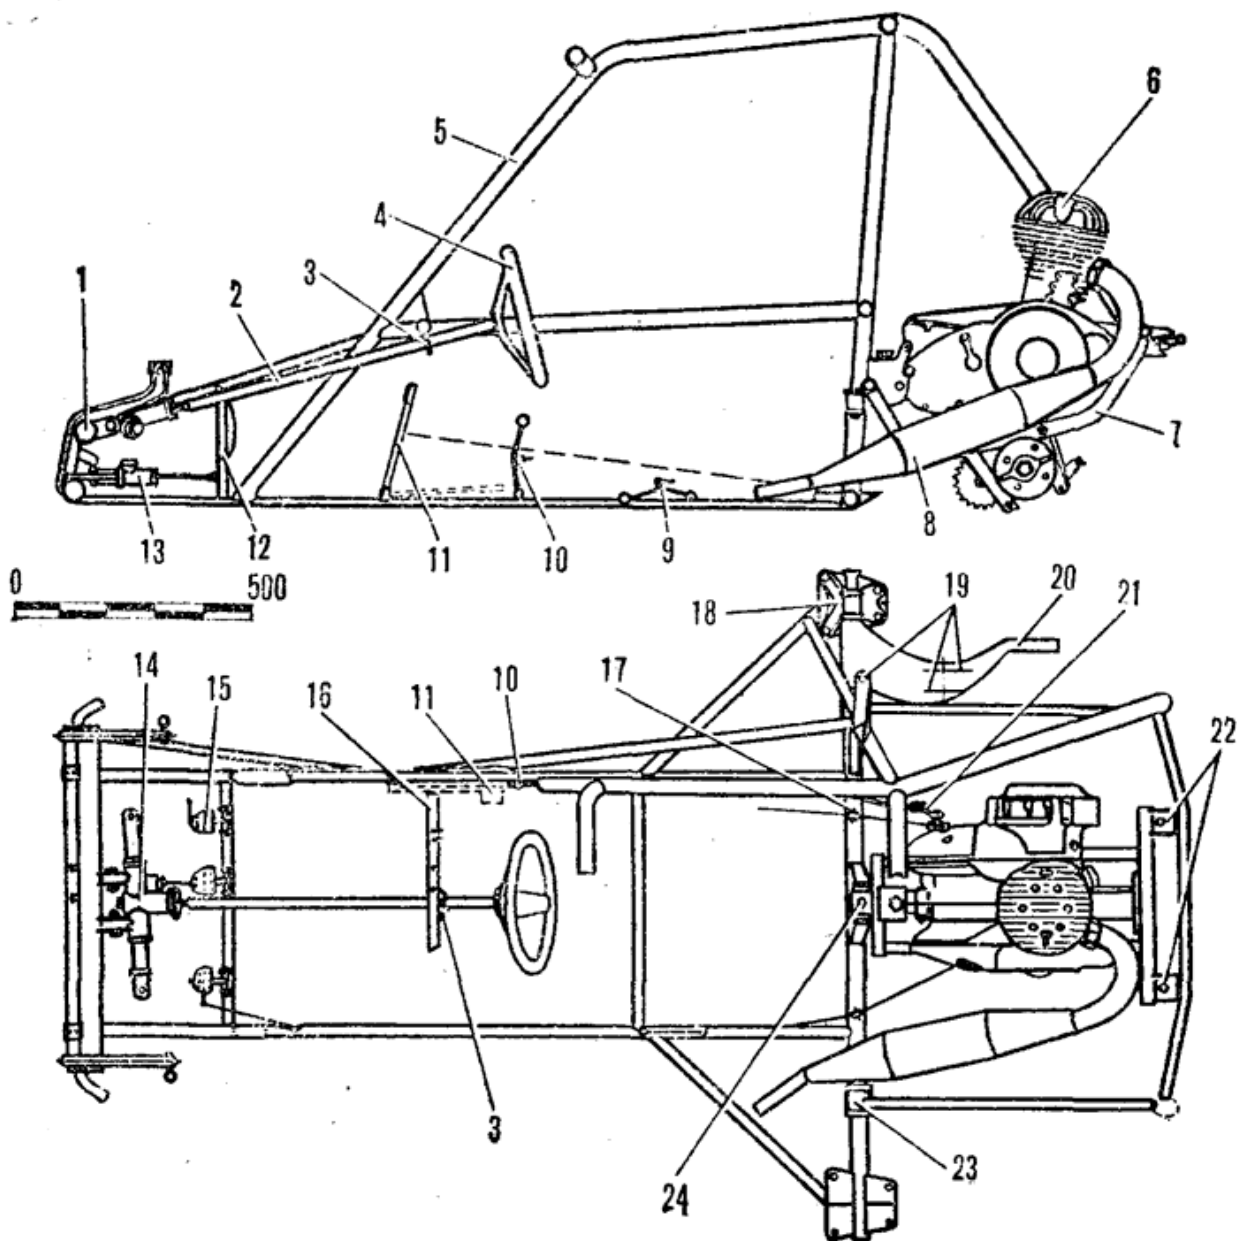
Компонування основних агрегатів: 1 - передня підвіска, 2 - вал кермового колеса, 3 - шайба кермового вала, 4 - кермове колесо, 5 - рама, 6 - двигун, 7 - підрамник, 8 - вихлопна труба із глушителем, 9 - важіль реверса, 10 - важіль перемикання передач, 11 - педаль кик-стартера (пунктиром показане неробоче положення), 12 - педаль гальма, 13 - головний гальмовий циліндр, 14 - кермовий механізм, 15 - педаль керування дроселем карбюратора, 16 - щиток приладів, 17 - ролик троса кик-стартера, 18 - зовнішній шарнір задньої підвіски, 19 - вушка амортизатора, 20 - важіль задньої підвіски, 21 - важіль кик-стартера, 22 - задні кронштейни підвіски двигуна, 23 - внутрішній шарнір задньої підвіски, 24 - передній кронштейн підвіски двигуна.
